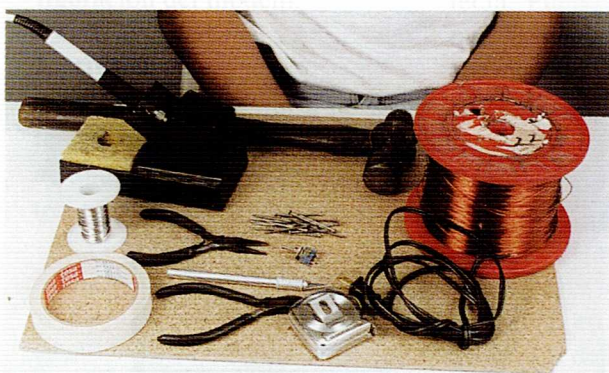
Materiales y herramientas para la bobina desmagnetizadora
